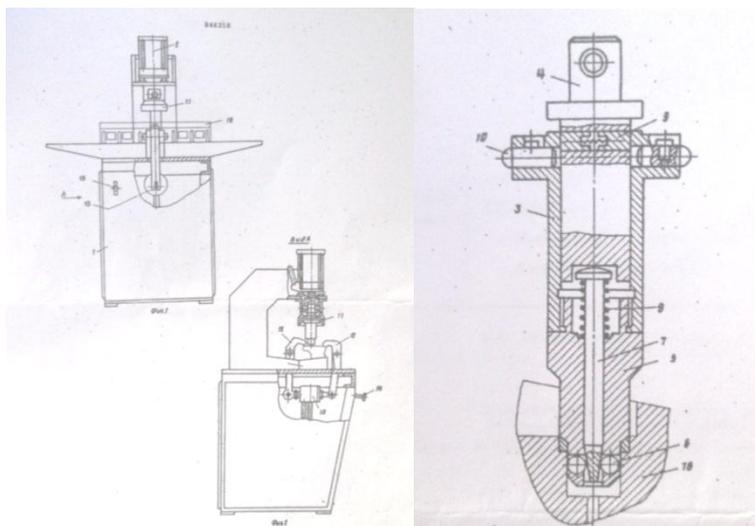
Стенд для выпрессовки деталей, выпрессовывающая
